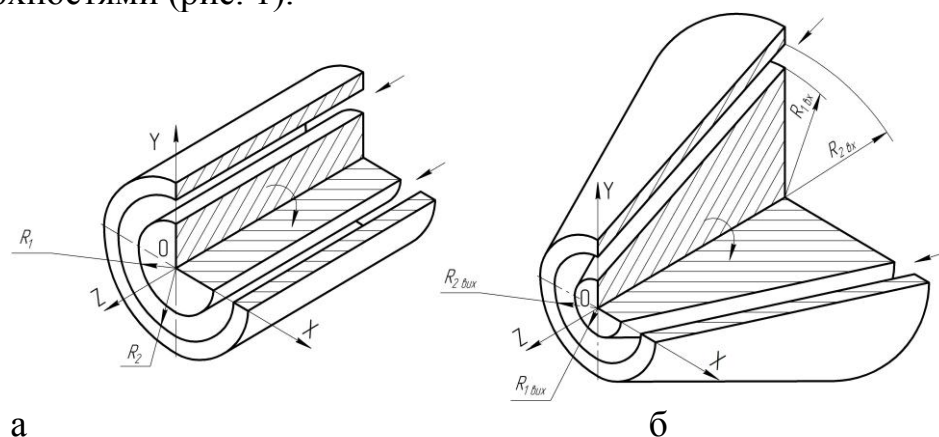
Схемы кольцевых каналов: а – цилиндрического, б – конического
